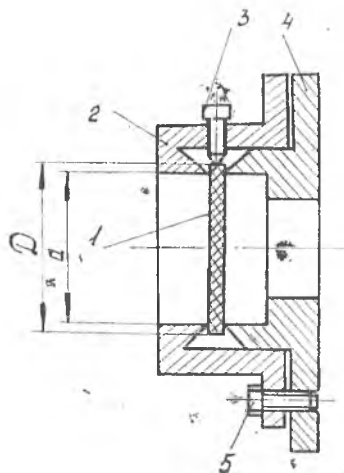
Схема крепления образца: 1 — образец; 2 — подвижная опора; 3 — установочные винты; 4 — неподвижная опора; 5 — крепежные винты
